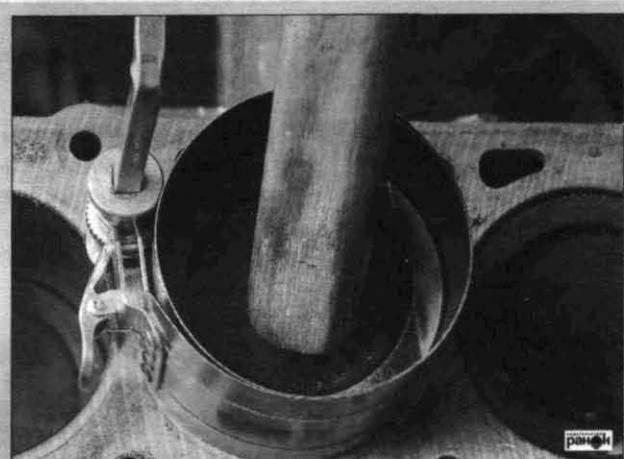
Установка поршня в цилиндр при помощи приспособления
